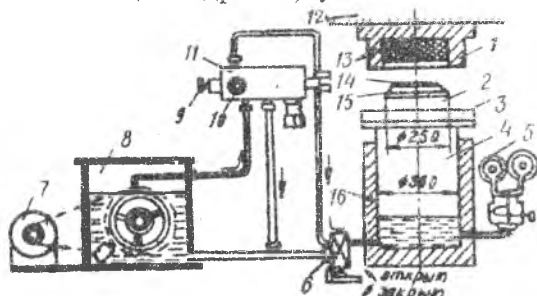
Схема лабораторного прессы для штамповки эластичной средой
